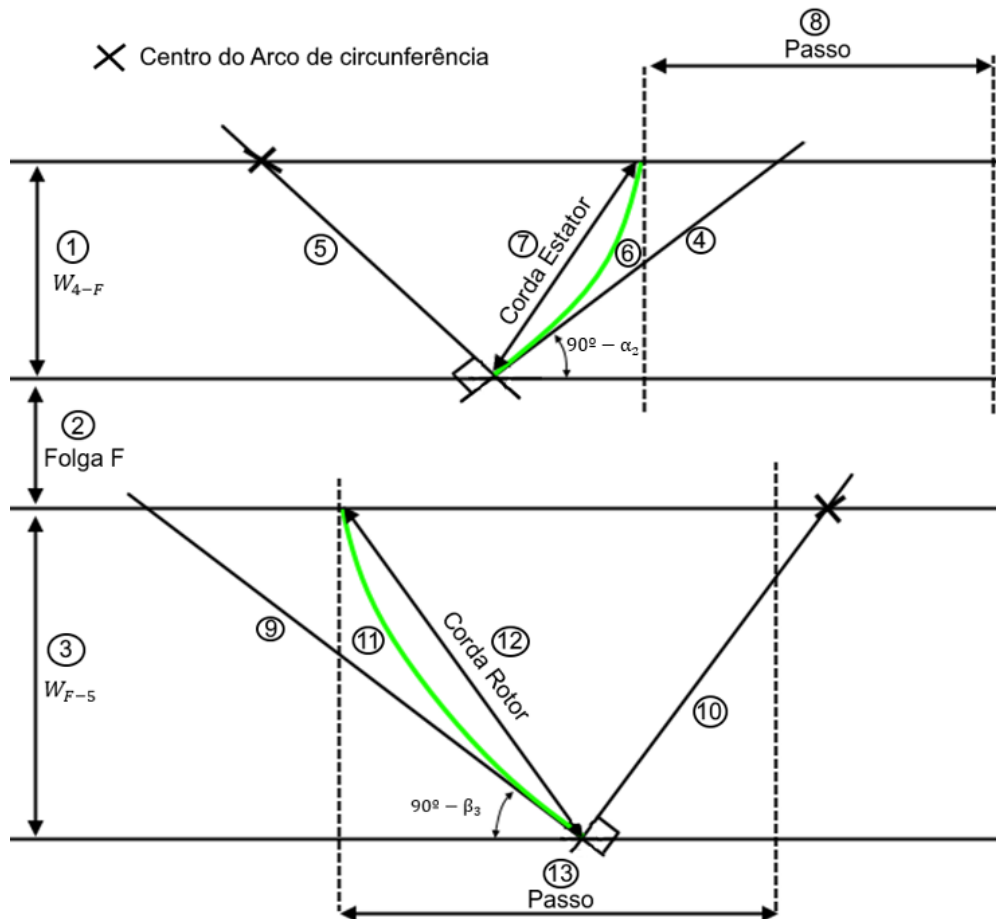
Desenho das pás do estator e rotor da turbina
